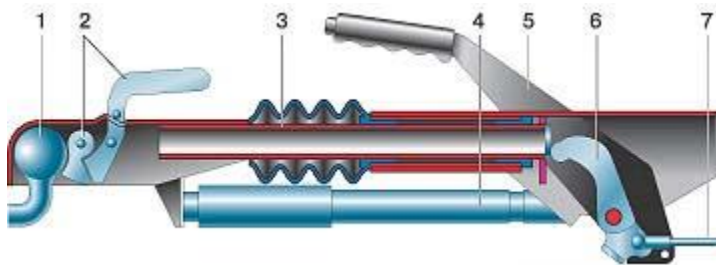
Узел сцепки и устройство управления тормозами: 1 - шар ТСУ; 2 - запорный механизм; 3 - поршень; 4 - амортизатор; 5 - рукоятка стояночной тормозной системы; 6 - рычаг привода рабочей тормозной системы; 7 - трос привода тормозов.
